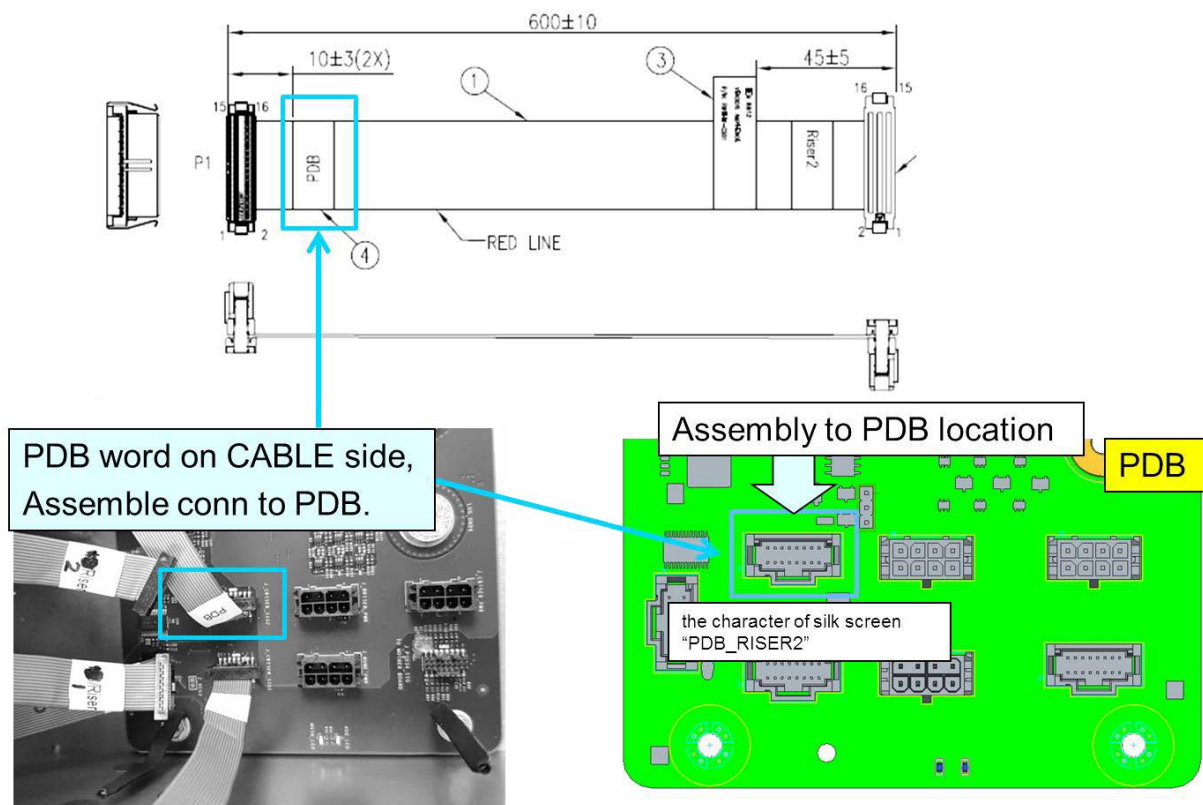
Assemblage du câble IDC, carte de montage 2-PDB, vers PDB
